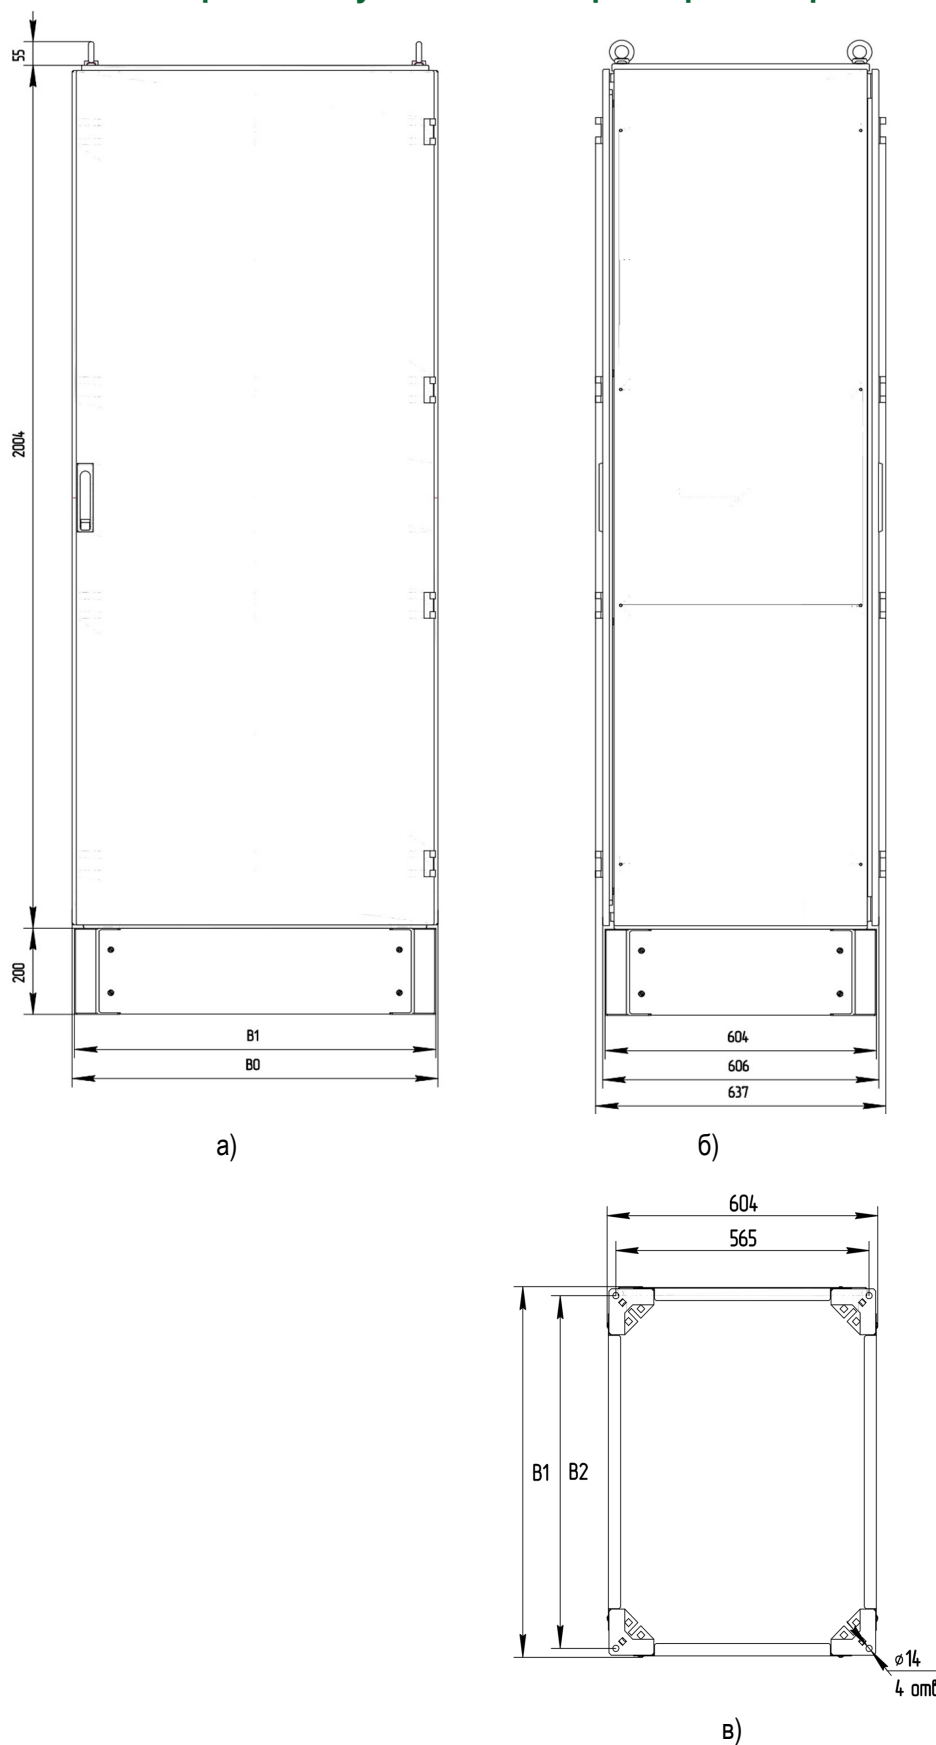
Внешний вид, габаритные и установочные размеры шкафа с одностворчатой дверью
